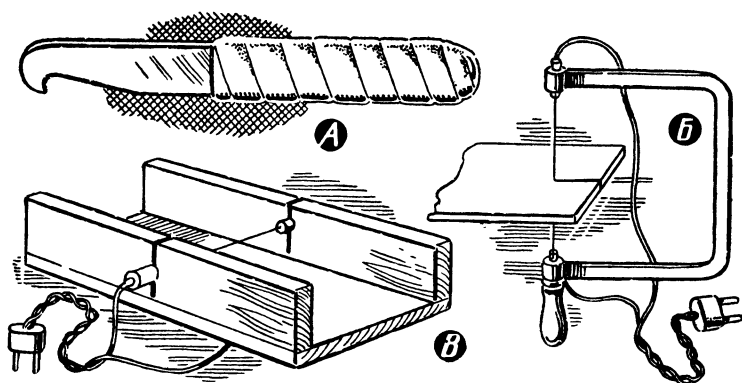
Инструмент для обработки пластмасс: А — резак; Б — специальный резак; В — станок для резки пенопласта.
